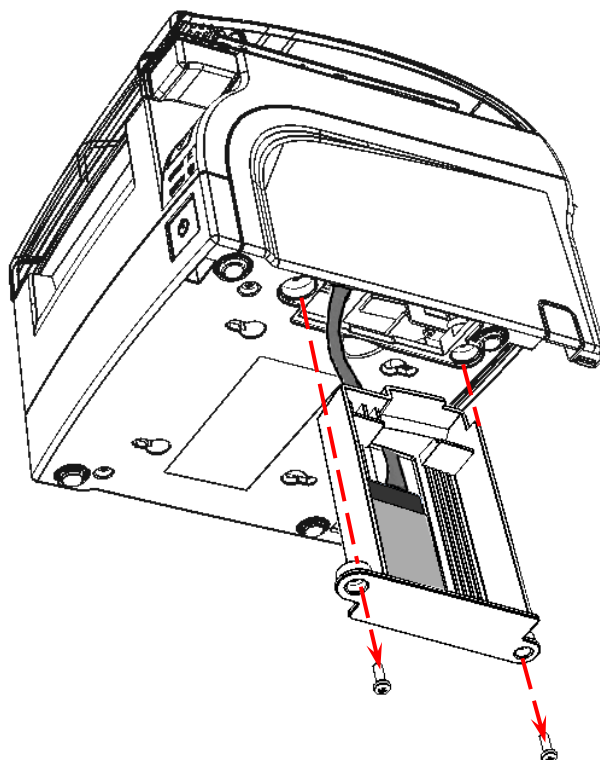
Извлечение отсека для ФН из корпуса ККТ
